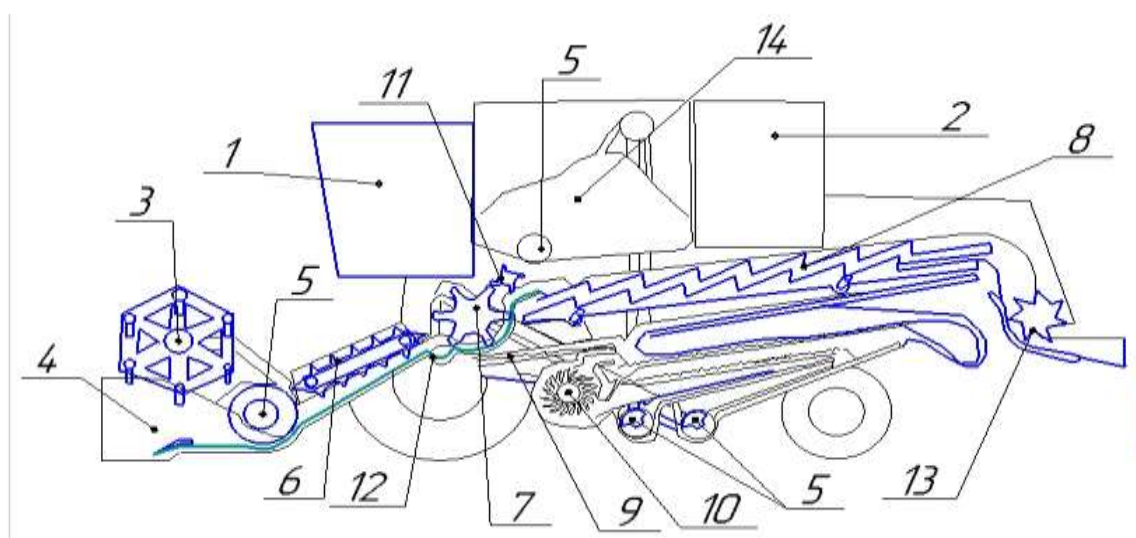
Схема основных частей зерноуборочного комбайна
